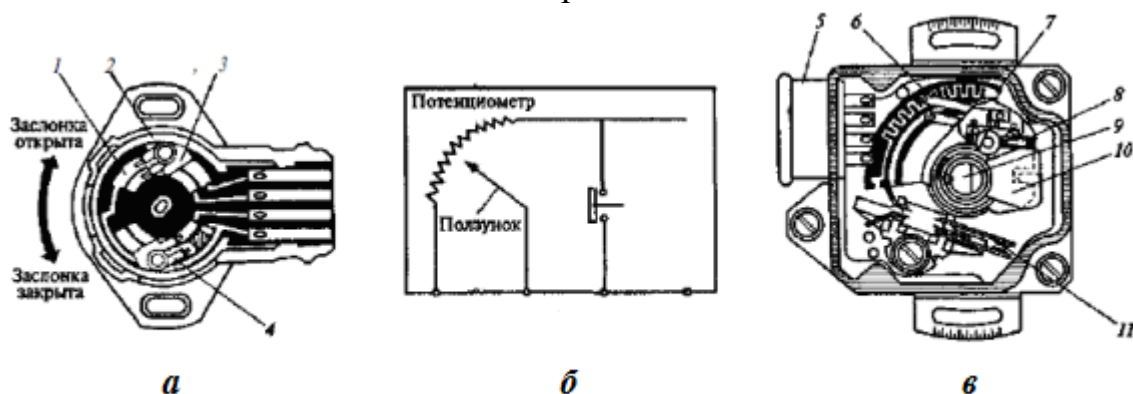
Датчики угла поворота дроссельной заслонки: а – реостатный; б – потенциометрический; в – дискретный; 1 – резистивный элемент; 2 – корпус; 3, 4 и 6 – ползунки; 5 – кабельный разъем; 7 – контактная пластина; 8 и 11 – контактные группы; 9 – привод; 10 – кулачок
